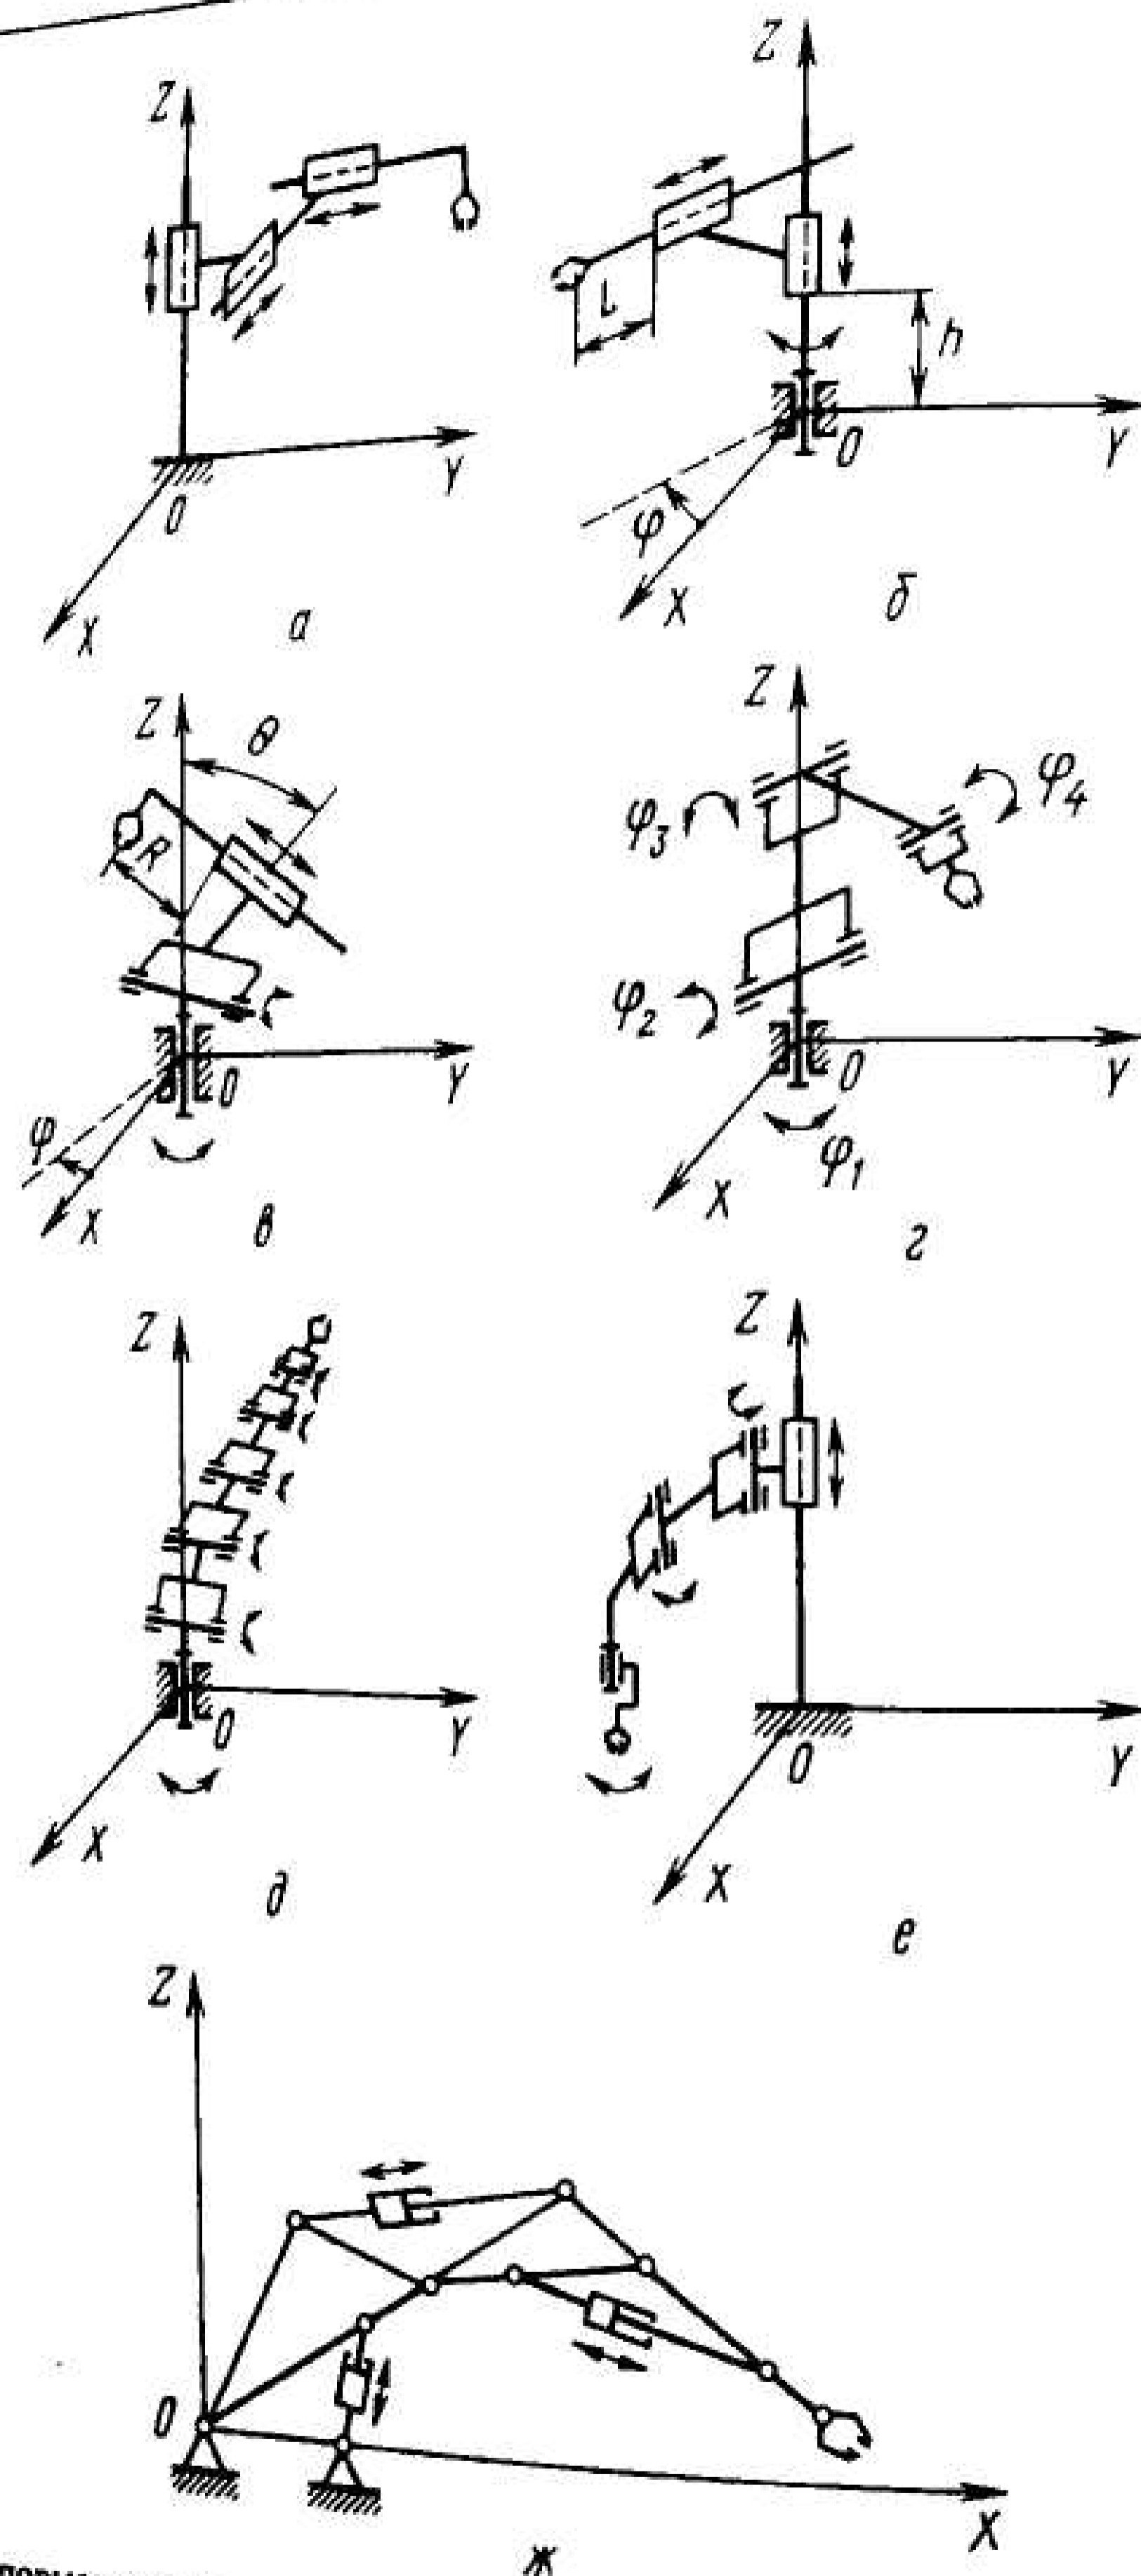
Типовые кинематические схемы манипуляторов: а — прямоугольная; б — цилиндрическая; в — сферическая; г — антропоморфная; д — с избыточностью; е — SCARA; ж — схема гидравлического манипулятора с ветвлением кинематической цепи
